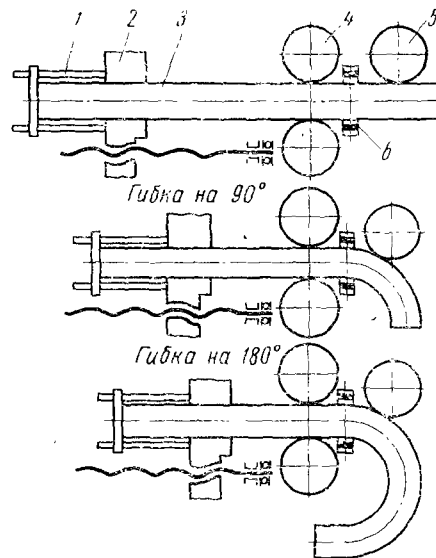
Схема трубогибочного станка с индукционным нагревом:
